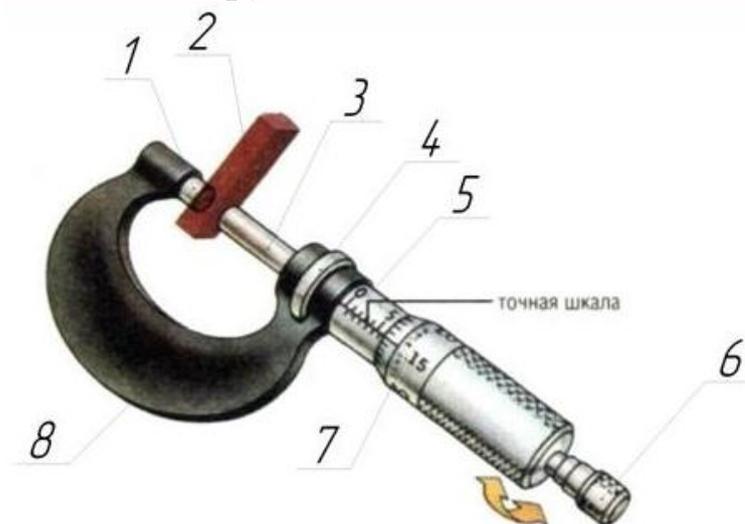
Гладкий микрометр МК: 1 – неподвижный упор («пятка»); 2 – измеряемый предмет; 3 – подвижный шпиндель (микрометрический винт); 4 – кольцевая гайка; 5 – полый стебель; 6 – винт трещотки; 7 – барабан (гильза); 8 – скоба
